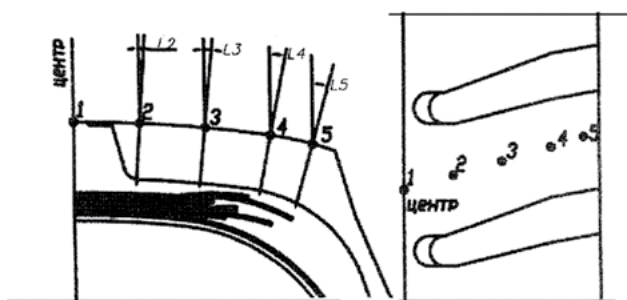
Схема сверления шины размера 33.00 R51 мод. Бел-162 для замера температуры
